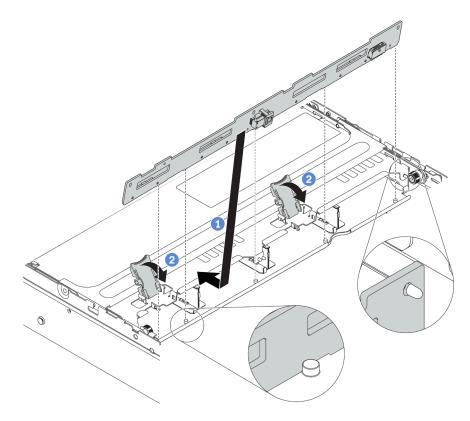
Installazione del backplane dell'unità centrale da 3,5"
